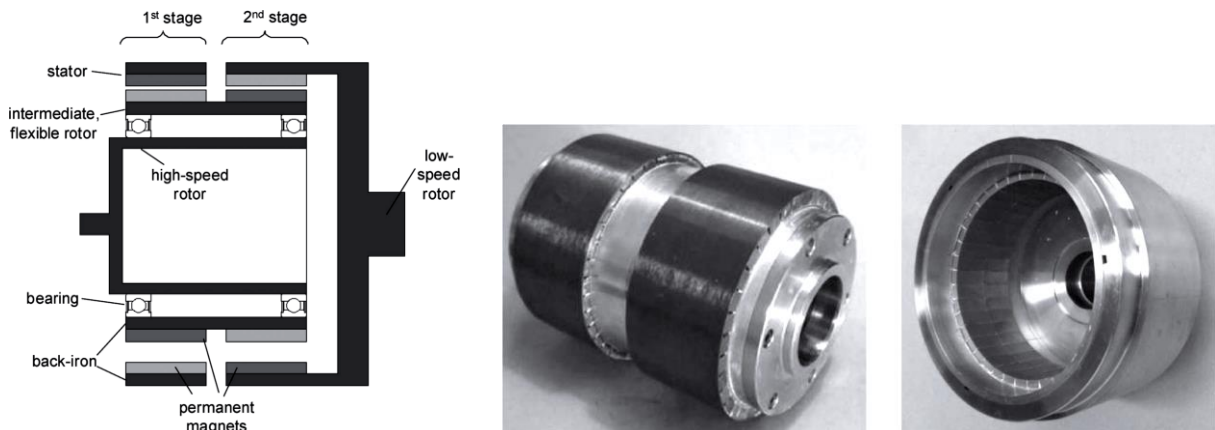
Prototype d'engrenage harmonique à deux étages [REN10].
